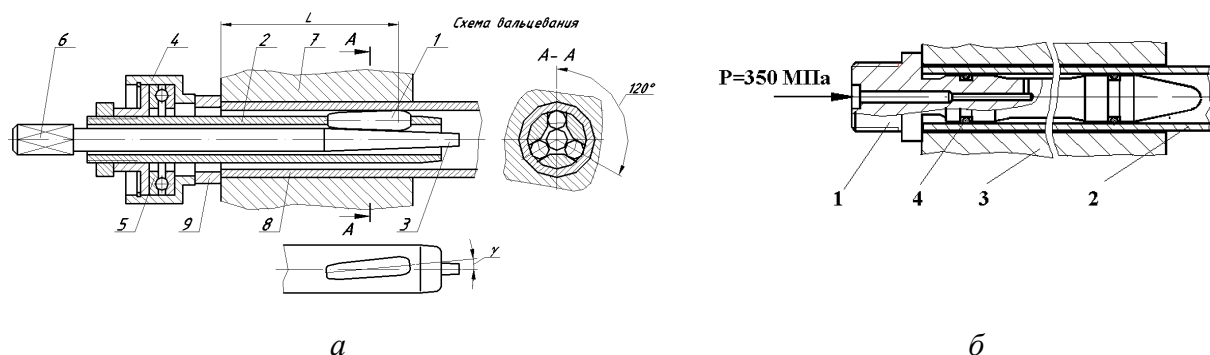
Методы закрепления: *а* - роликовое вальцевание: 1- ролики; 2- корпус; 3- веретено; 4-обойма; 5- подшипник; 6- хвостовик; 7-доска трубная; 8- труба; *б* - гидрораздача: 1- зонд; 2- труба; 3- доска трубная; 4- уплотнительные кольца)
